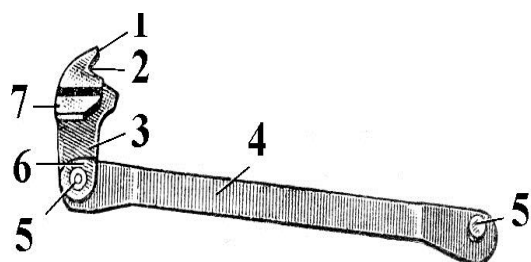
Спусковая тяга с рычагом взвода (1 — разобщающий выступ рычага взвода; 2 — вырез; 3 — рычаг взвода; 4 — спусковая тяга; 5 — цапфы спусковой тяги; 6 — пяточка рычага взвода; 7 — выступ самовзвода)
